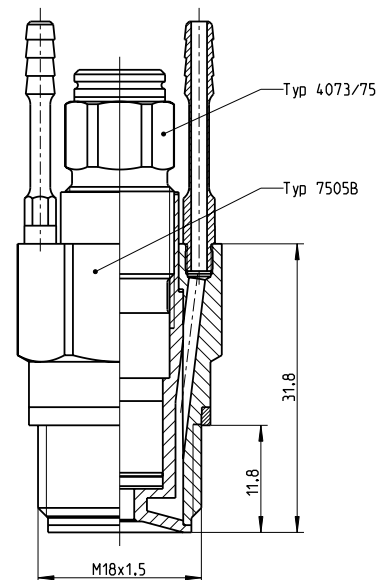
Einbau des Sensor Typs 4075A... in Kühladapter Typ 7505B
